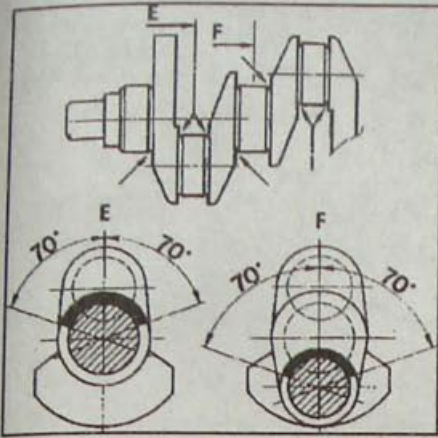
Расположение зоны коленчатого вала с углом 140° , которую нельзя перешлифовывать (участки E и F выбраны в качестве примера)
